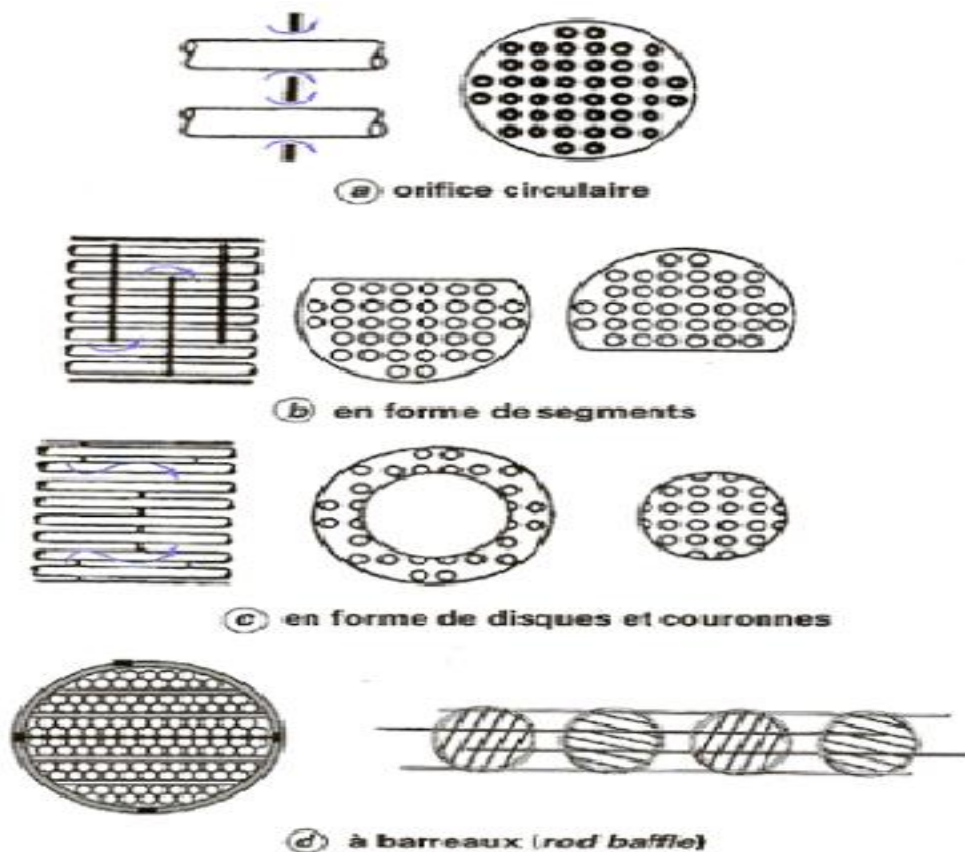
définition de quatre formes d'échangeur à tube et calandre
